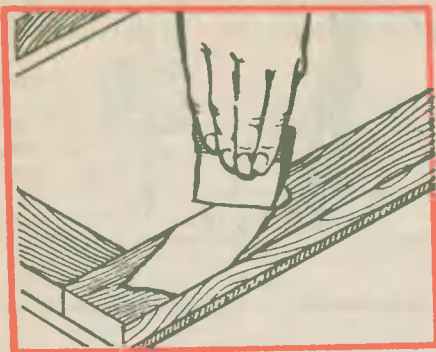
Все дефекты скрост шпаклевка, разравниваемая шпателем — металлической или резиновой пластиной.
